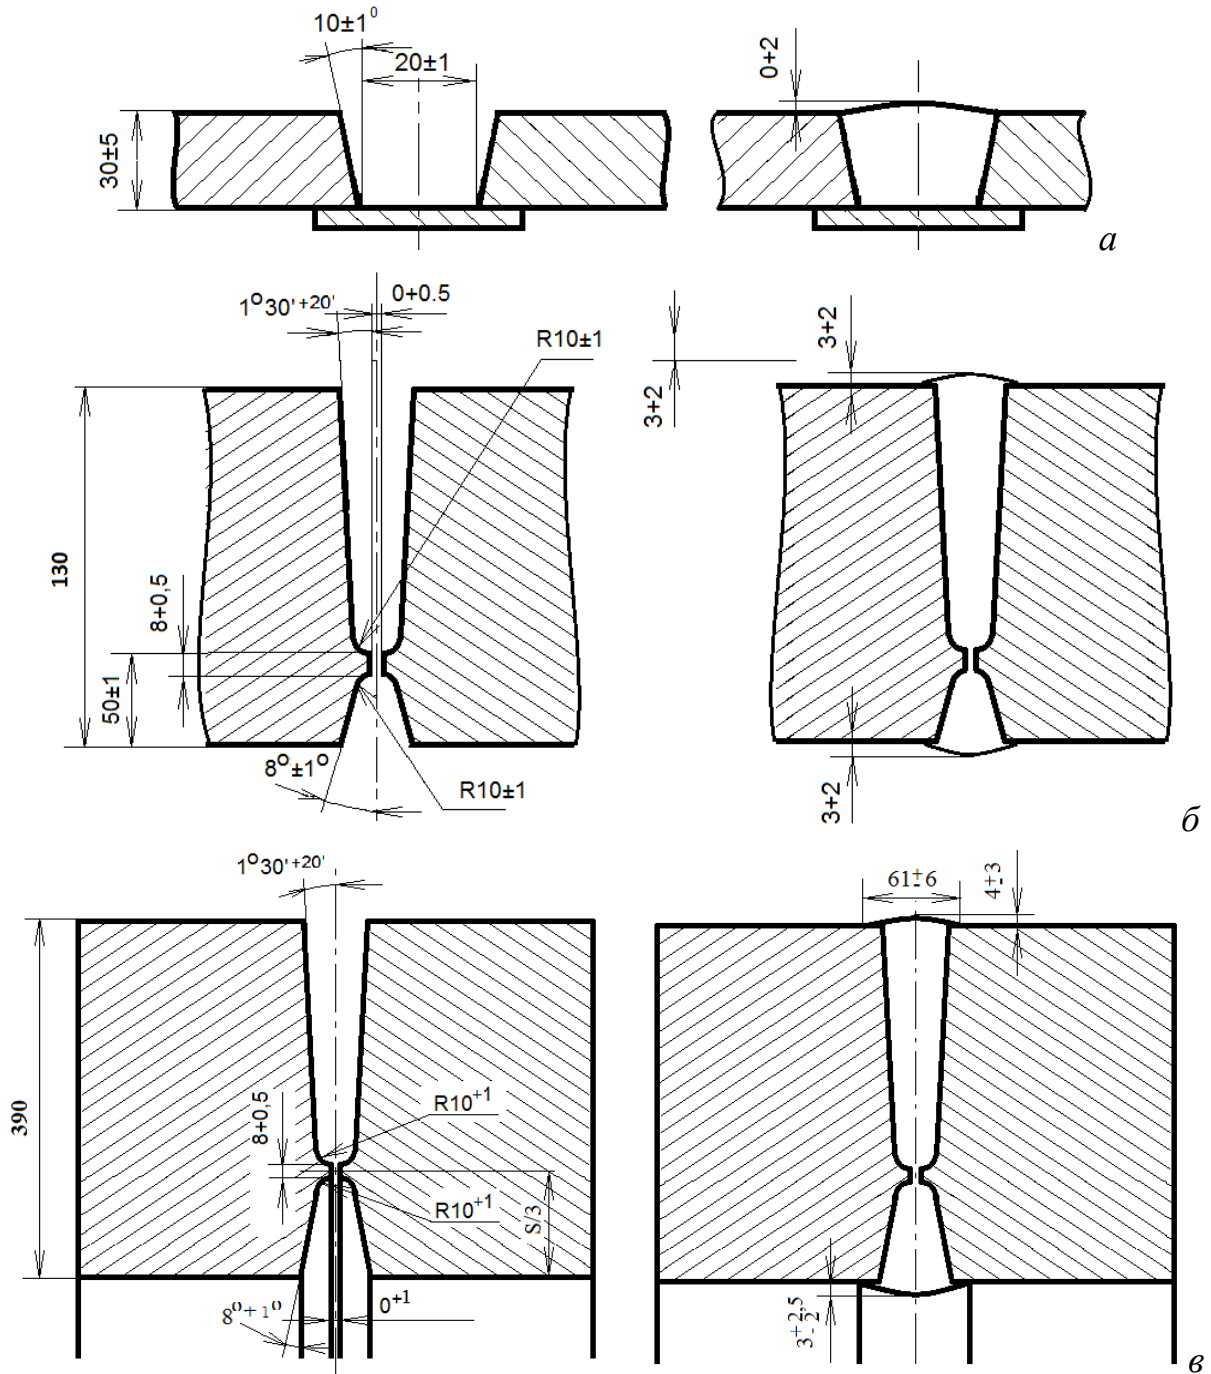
Конструктивные элементы подготовки кромок и сварных швов
